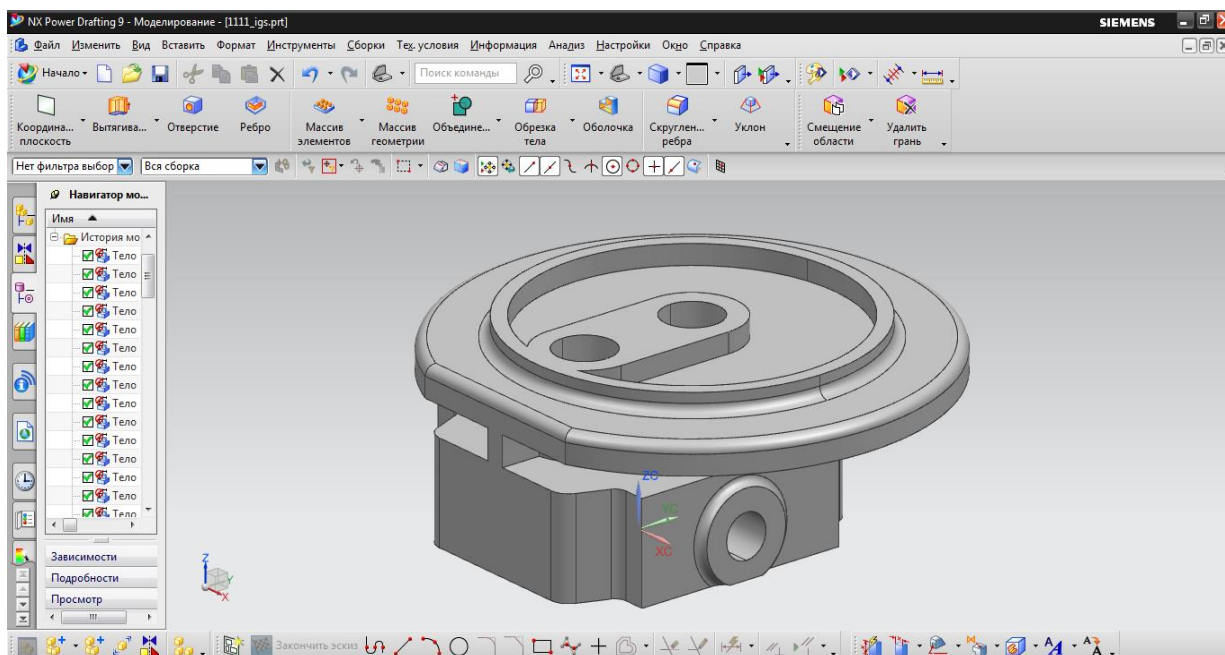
Деталь «Корпус клапану МПВ 349.003»
